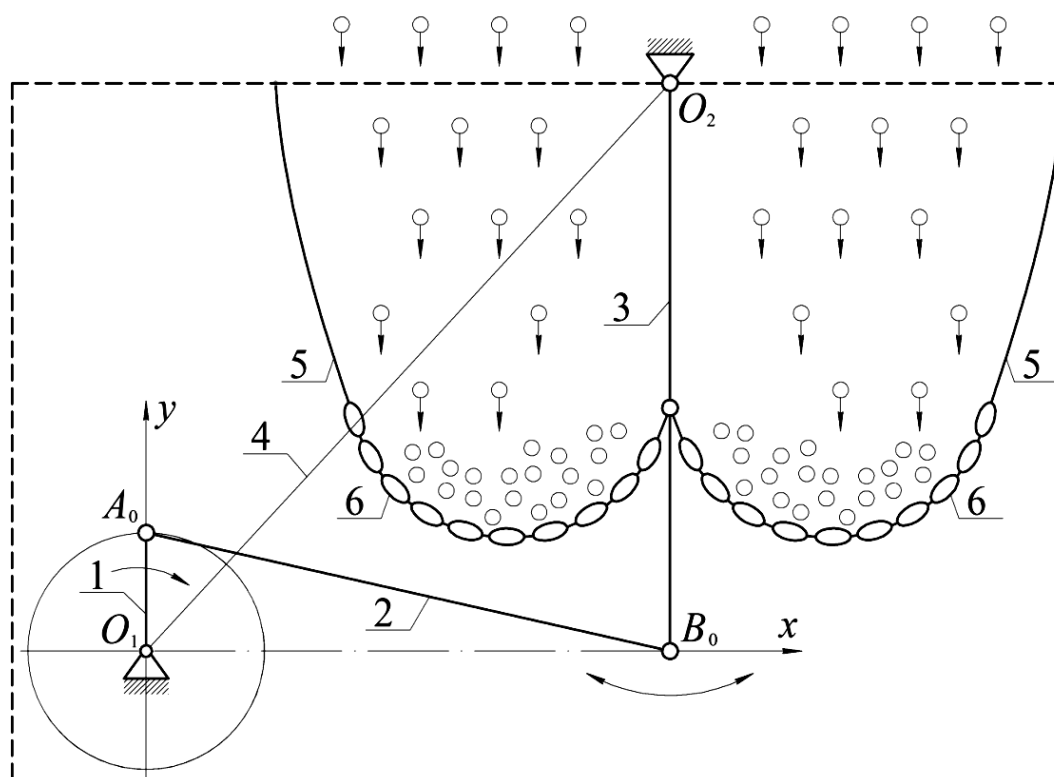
Приводной механизм и модель рабочей камеры цепного агрегата: 1 – кривошип; 2 – шатун; 3 – коромысло; 4 – стойка; 5 – эластичные стенки; 6 – цепные полотна
